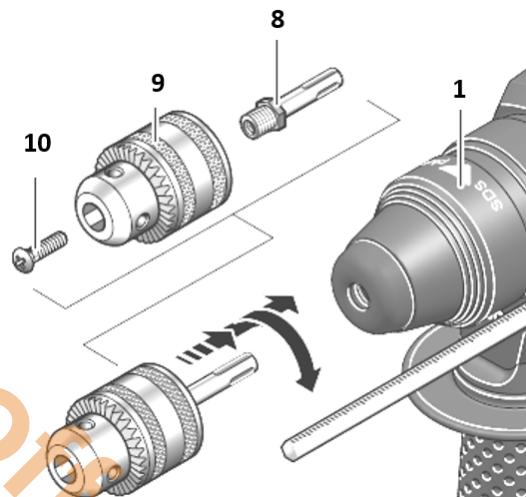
Установка патрона с зубчатым венцом.
